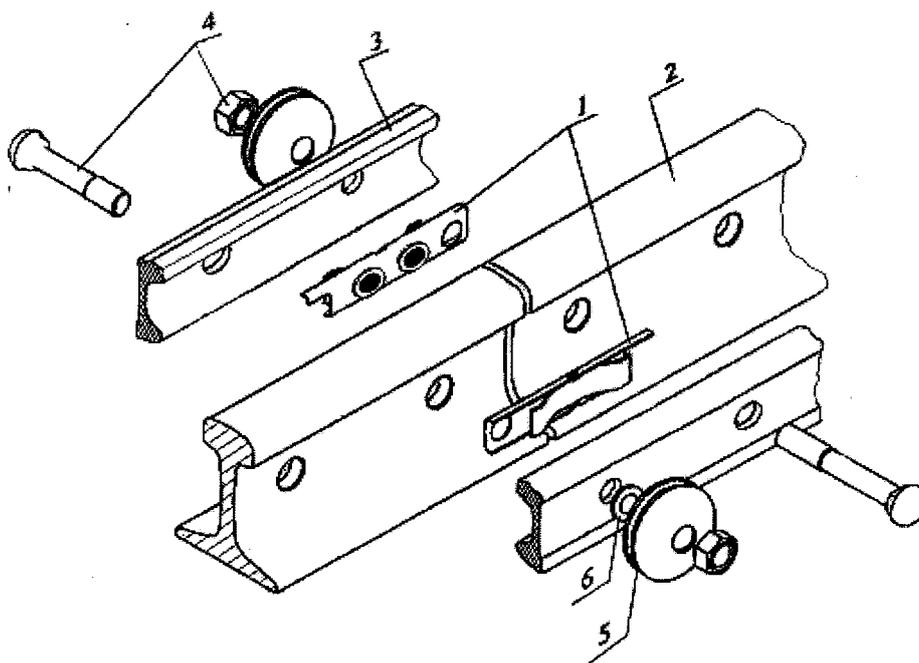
Соединитель рельсовый стыковой пружинный.
